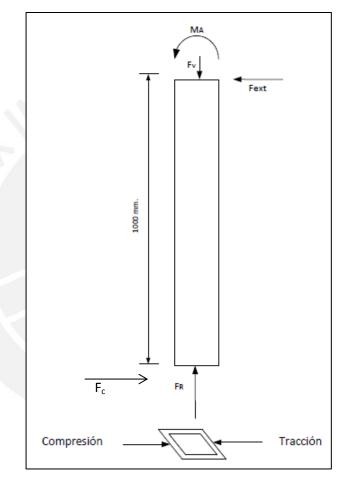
DCL de fuerzas y momentos en el cordón de soldadura Fuente: Elaboración propia
